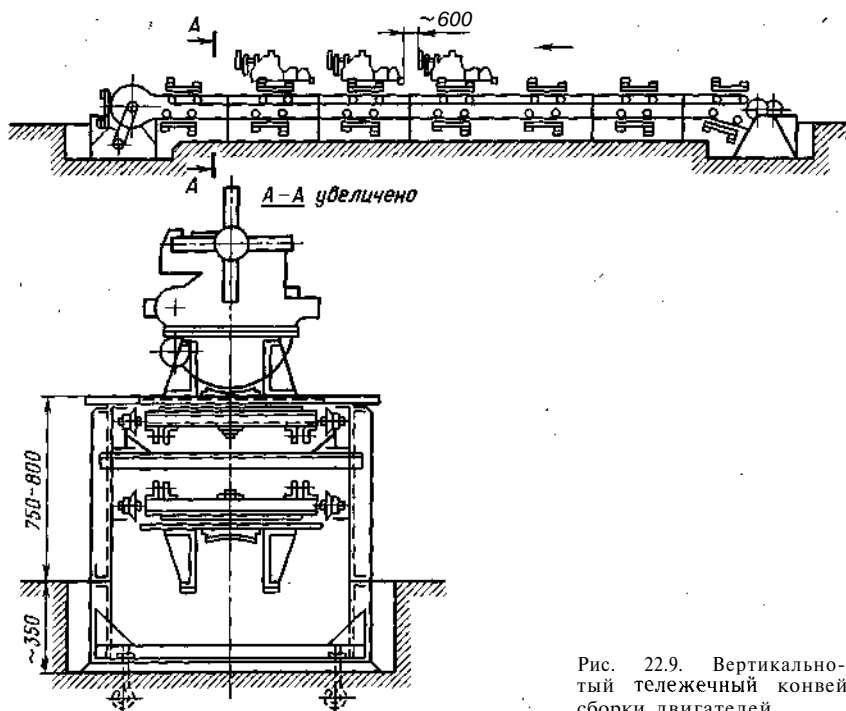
Вертикально-замкнутый тележечный конвейер для сборки двигателей
